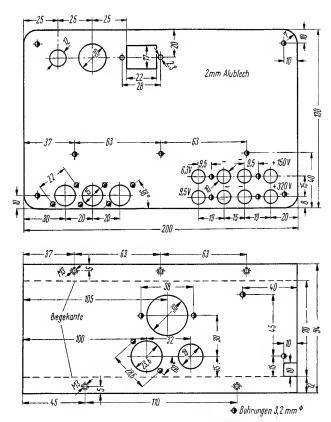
Maßskizze und Bohrplan für Frontplatte (oben) und Chassis (unten) des Universal-Netzgerätes
